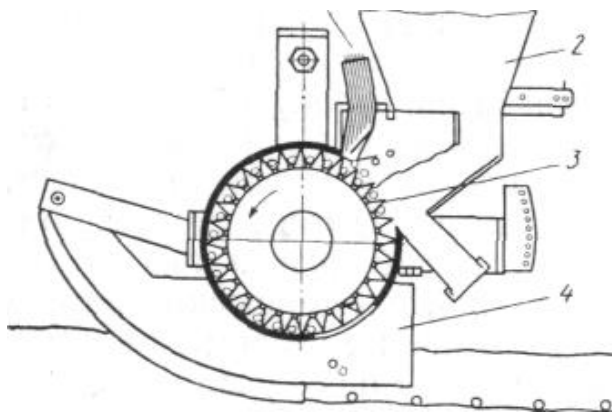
Висівний апарат сівалки «Аеромат»: 1- повітряний патрубок; 2- бункер; 3- висівний диск; 4- сошник.
